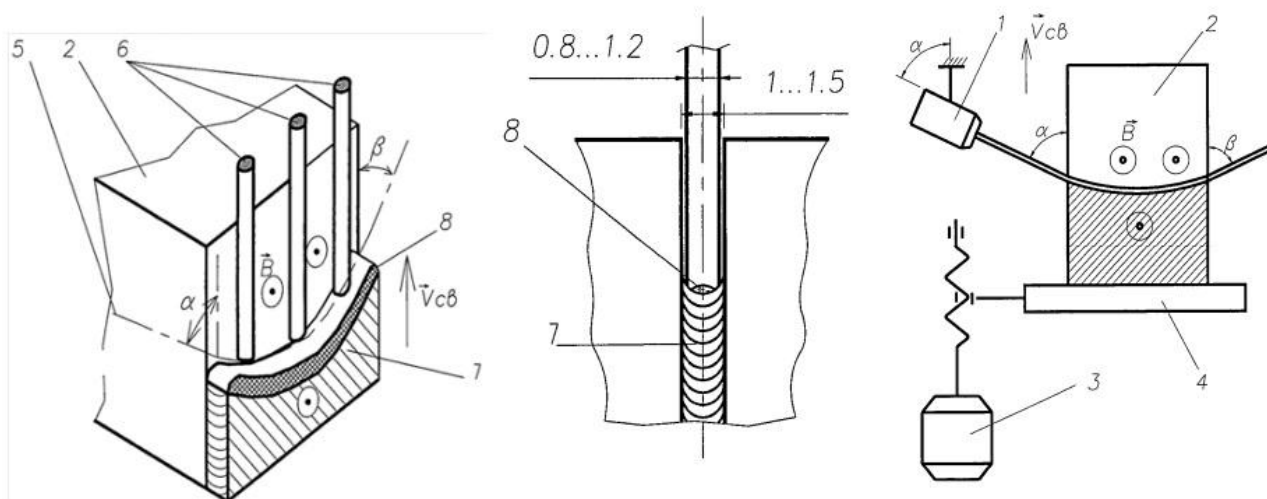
Сущность способа ЭЛС с присадочной проволокой: 1 – излучатель; 2 – свариваемые детали; 3,4 – механизм перемещения; 6 – присадочная проволока; 7 – сварной шов; 8 – сварочная ванна.
